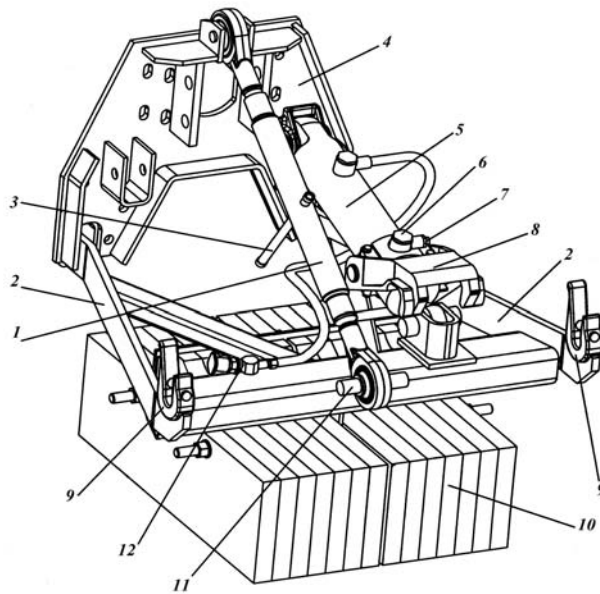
Переднее ПНУ УЭС-2-250А: 1 – тяга верхняя; 2 – рычаги нижние; 3 – рукоятка; 4 – плита; 5 – гидроцилиндр; 6 – угольник гидроцилиндра; 7 – заглушка; 8 – фиксатор; 9 – крюки; 10 – блок дополнительных грузов; 11 – палец; 12 – полумуфта наружная рукава гидроцилиндра
